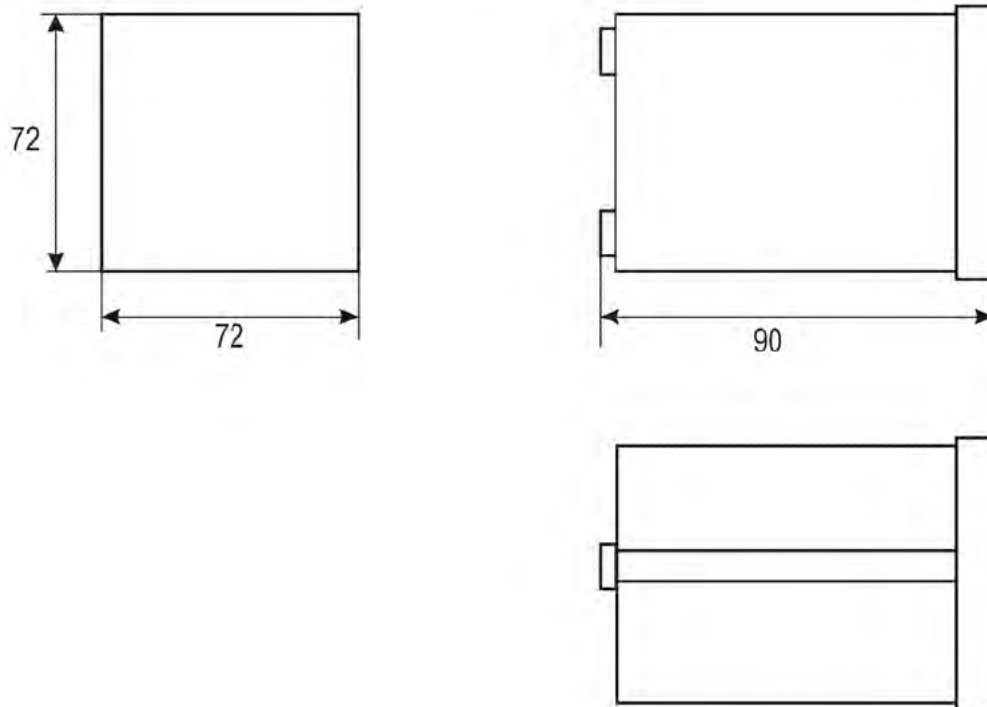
Габаритные размеры ИП для конструктивного исполнения М
